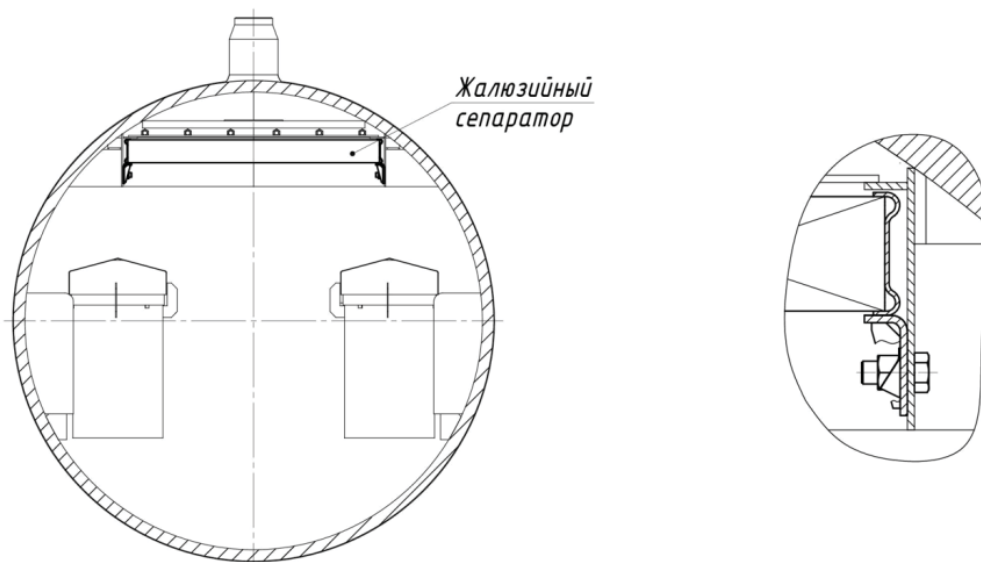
Поперечный разрез барабана и узел крепления жалюзийных сепараторов
